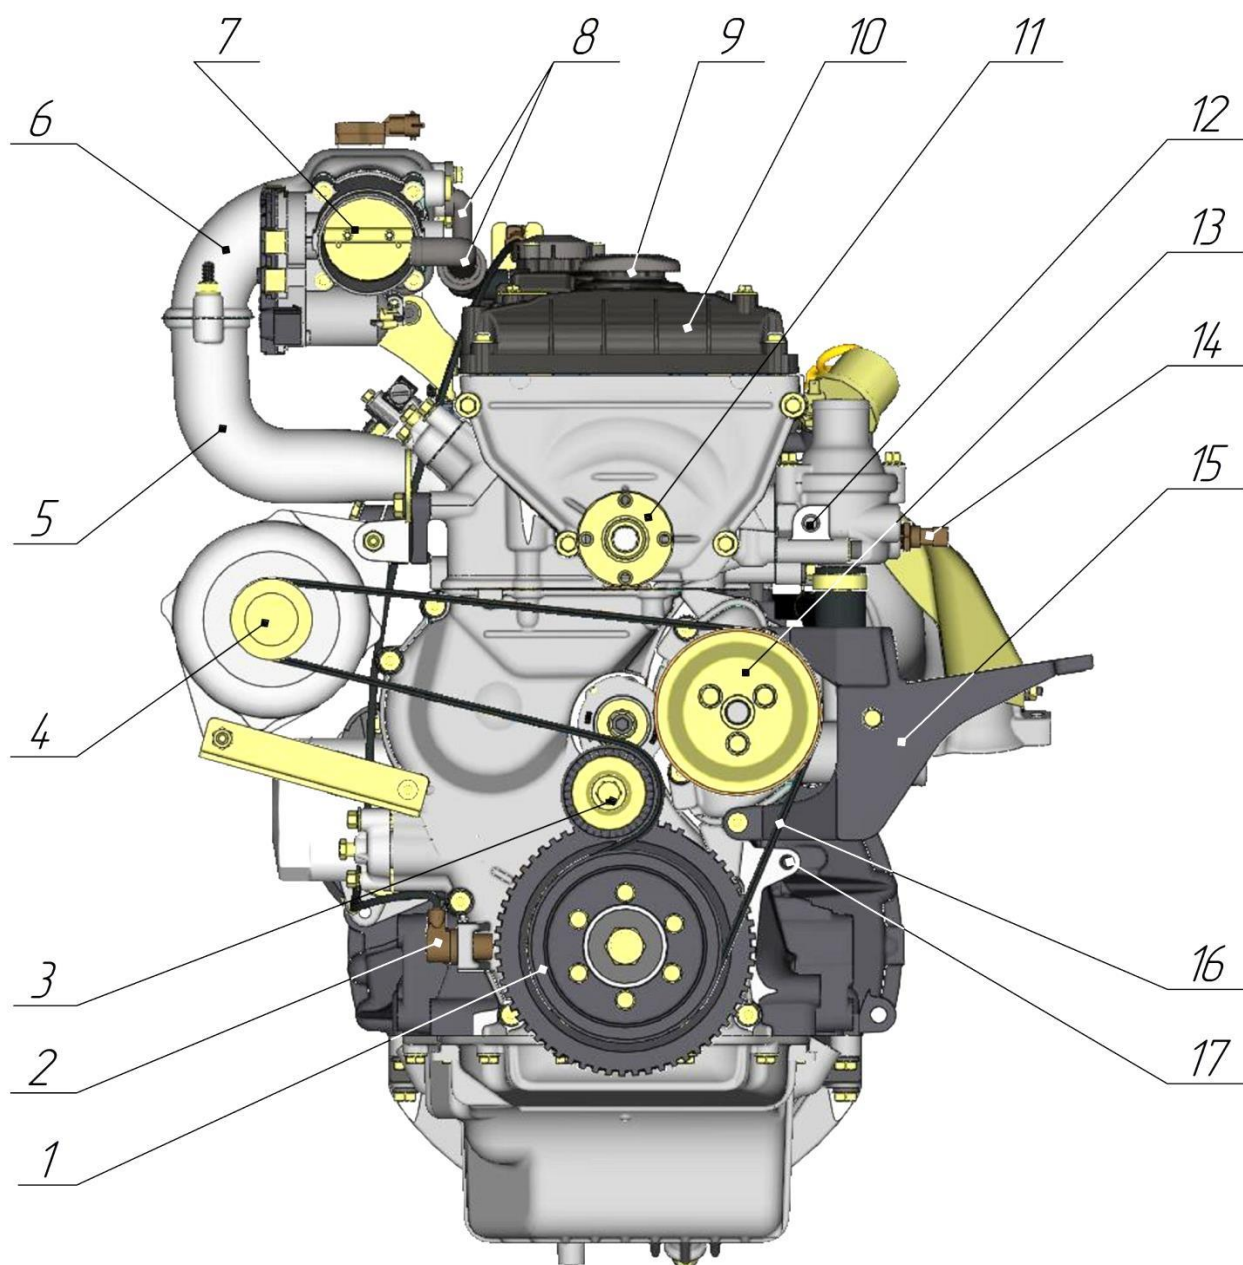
Вид спереди двигателя ЗМЗ-40905.10:
